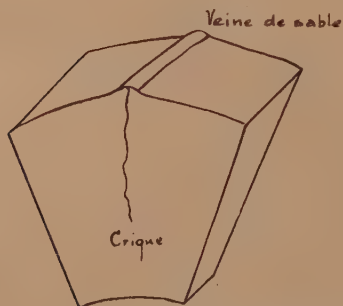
Crique soudée par apport de métal liquide et débouchant dans une veine de sable et d'acier.
